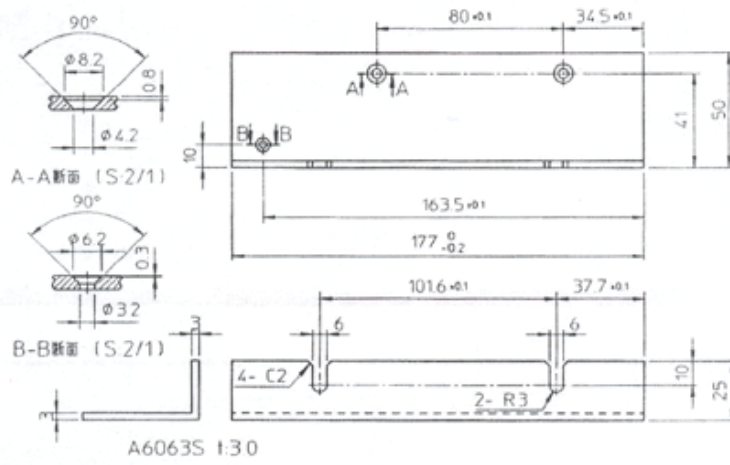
LUG MOUNT 金具 (EIA 规格 右用)
